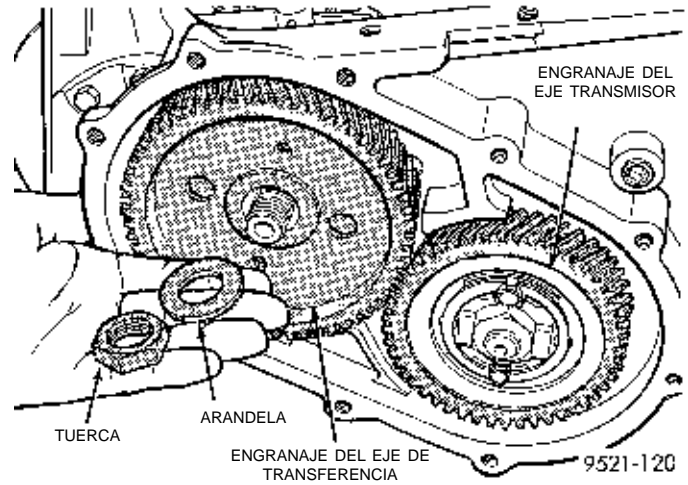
Tuerca y arandela del engranaje del eje de transferencia
